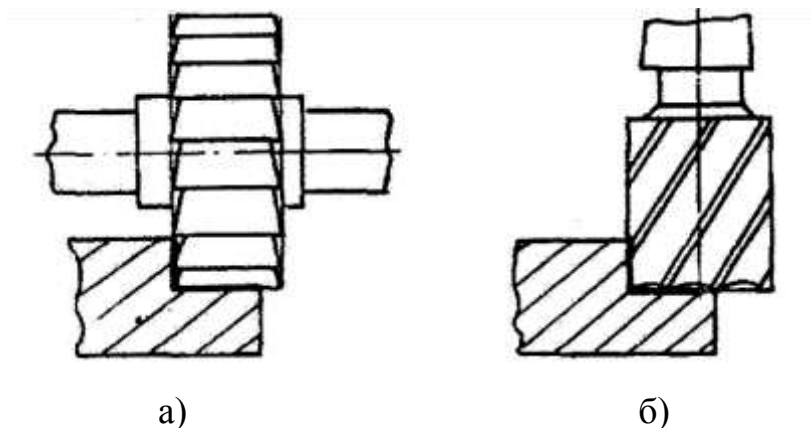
Фрезерование уступов дисковыми (а) и концевыми фрезами (б)
